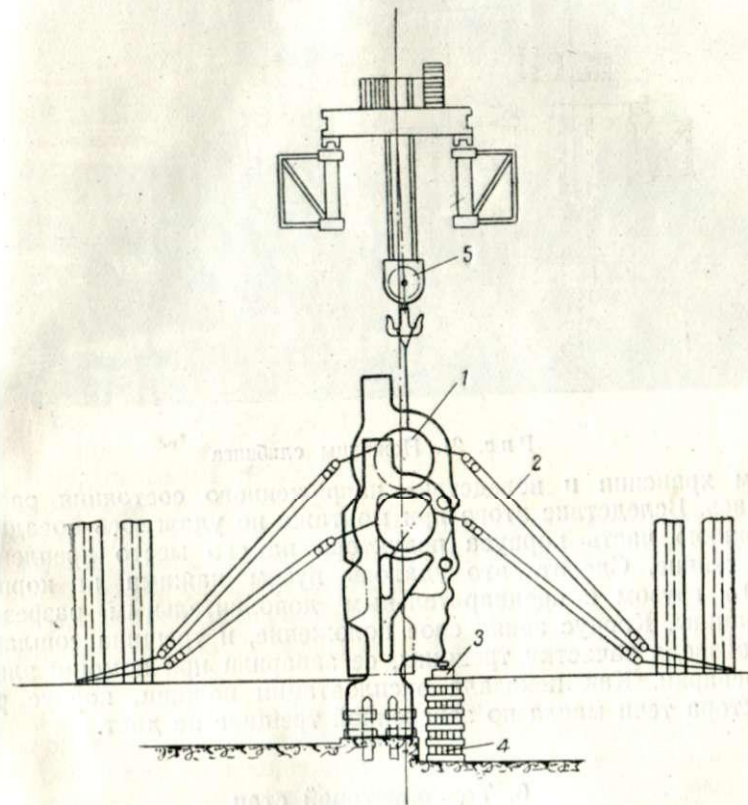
Схема подъема и установки станины ножниц в рабочее положение: 1—станина; 2—растяжки; 3—гидравлический домкрат; 4—шпальная клетка; 5—грузовой крюк мостового крана
